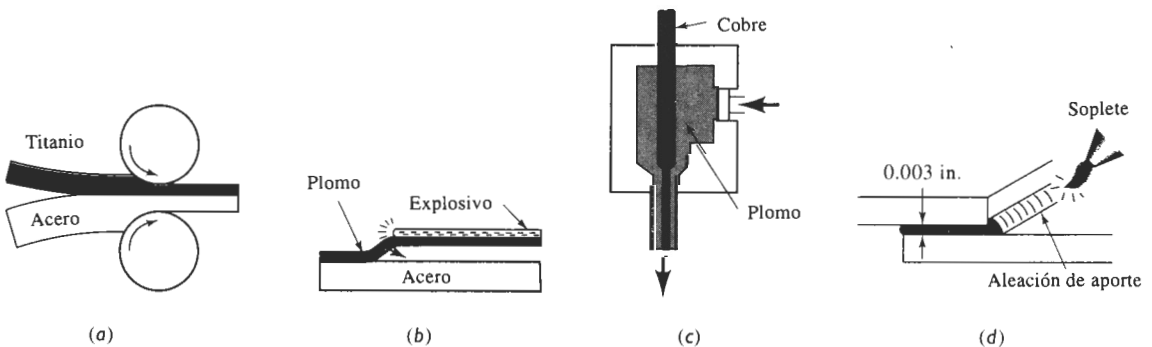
Técnicas para la producción de compuestos laminares: (a) unión por laminación, (b) unión por explosión, (c) coextrusión y (d) soldadura por capilaridad y difusión.
